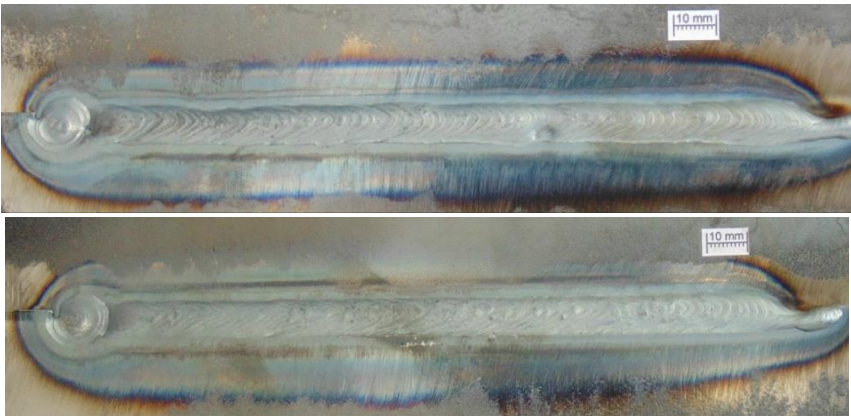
Soldagem de chapas sobrepostas com oscilação *switch back* de acordo com a Tabela 7
